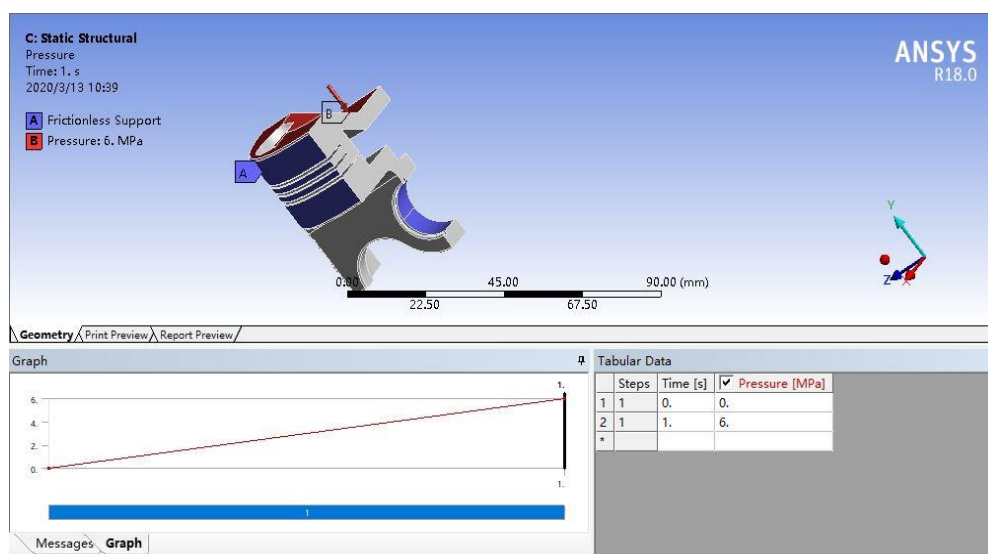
3D-модель конструкции рассматриваемого двигателя, включая рабочее напряжение на поршень
